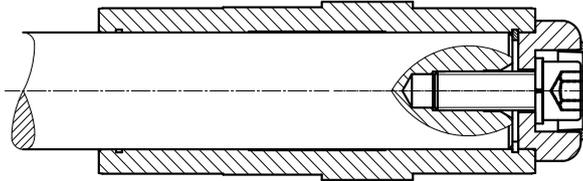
riduttore fissato ad un albero senza spallamento mediante elemento di fissaggio
